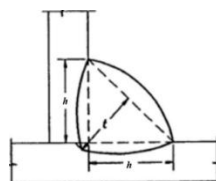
Ancho de garganta t y longitud de pierna h de la soldadura en filete [14].
